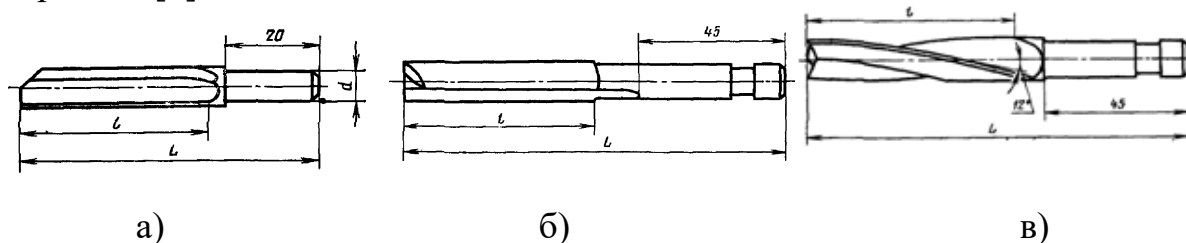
Фрезы дереворежущие концевые цилиндрические по ГОСТ 8994—80:
